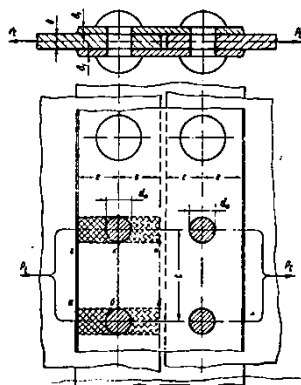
Схема нагружения конструкции соединения с двумя накладками.
